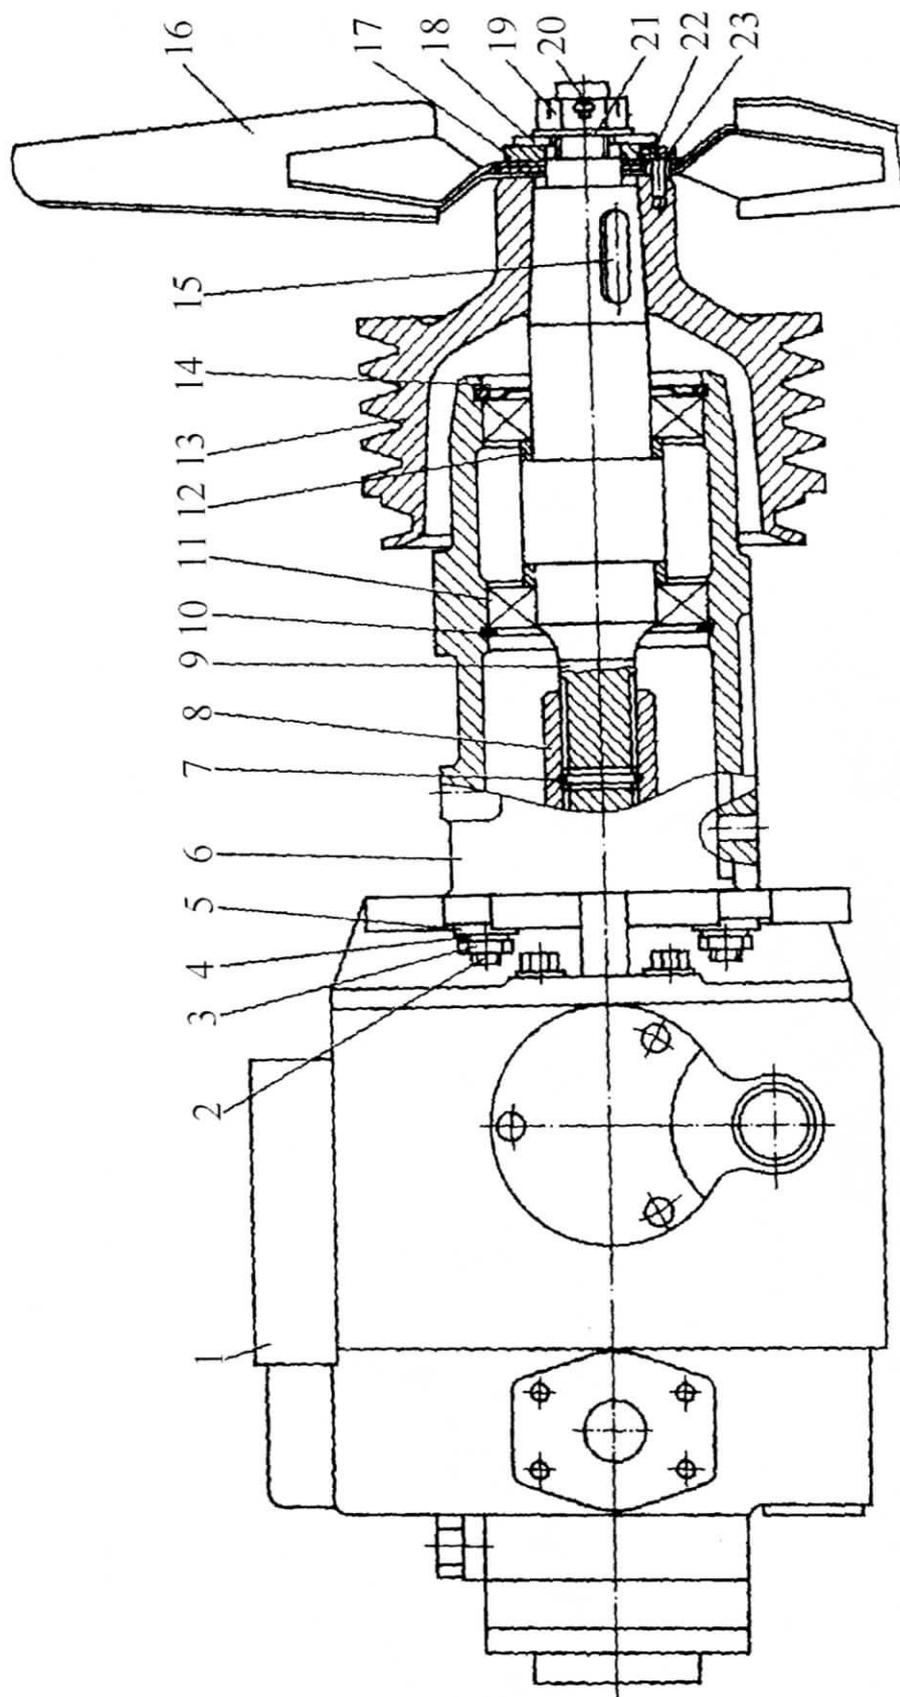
Установка гидронасоса привода ходовой части:
